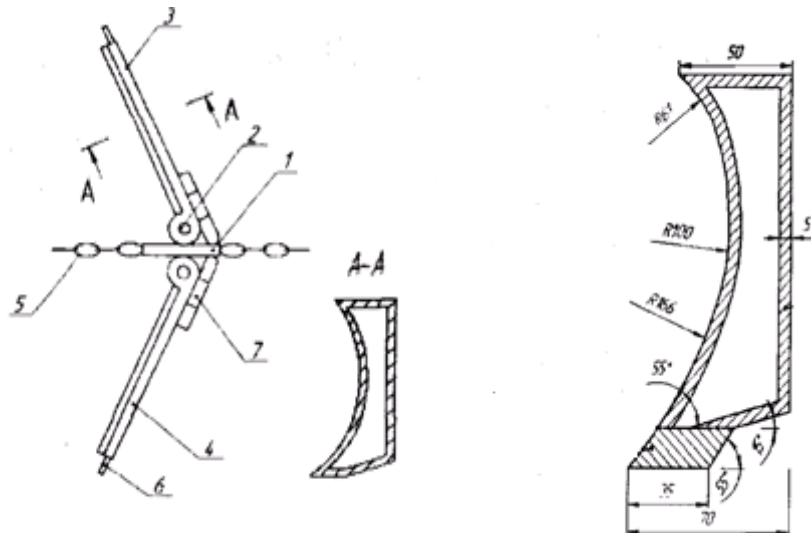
Загальна схема скреперного пристрою для прибирання гною: 1 – повзун; 2 – поворотний пристрій; 3, 4 – скребок; 5 – ланцюг; 6 – гумовий чистик; 7 – упор.
